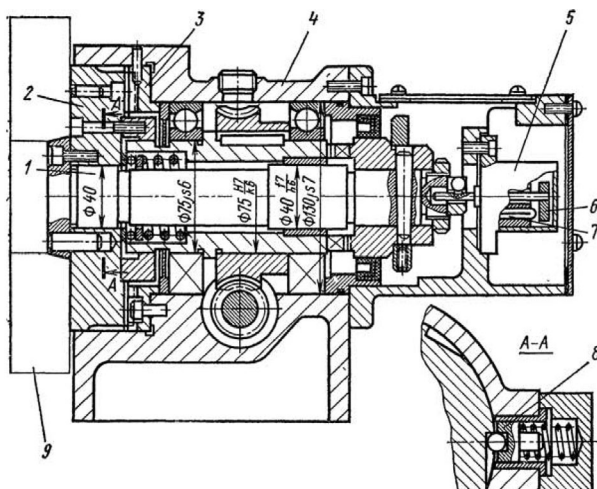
Ревolverная головка токарно-винторезного станка с ЧПУ 16K20Ф3 [7]:
